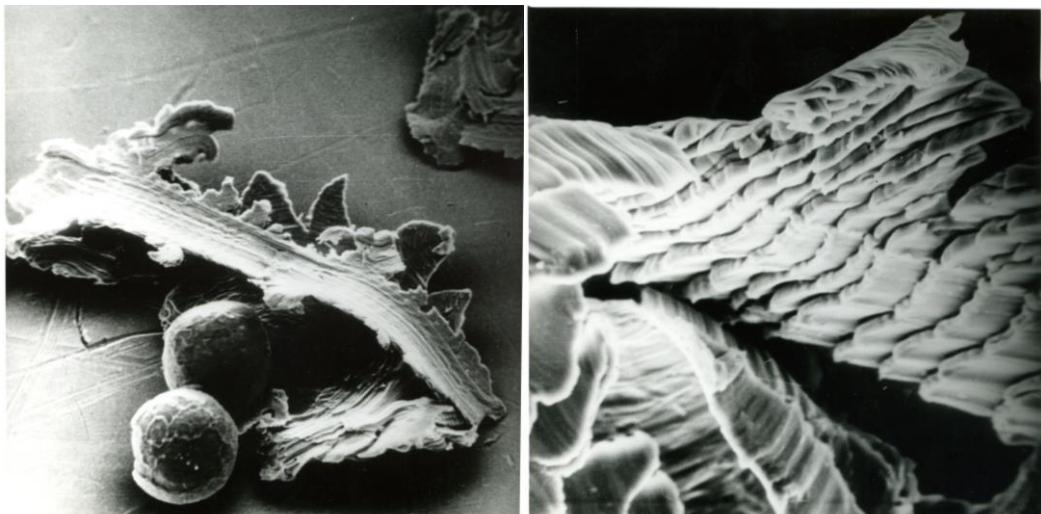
Фотоснимки микростружек, образующихся при шлифовании прерывистыми кругами с разным числом режущихся выступов
